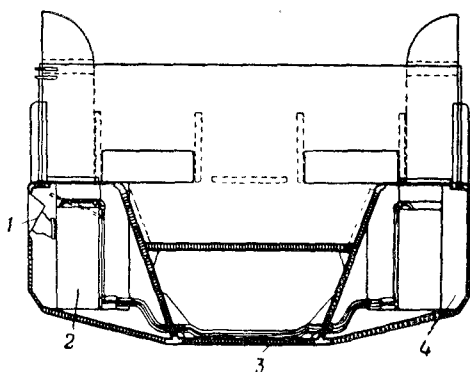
Конструкция корпуса плавающего четырехкольного автомобиля ХМ-521:
